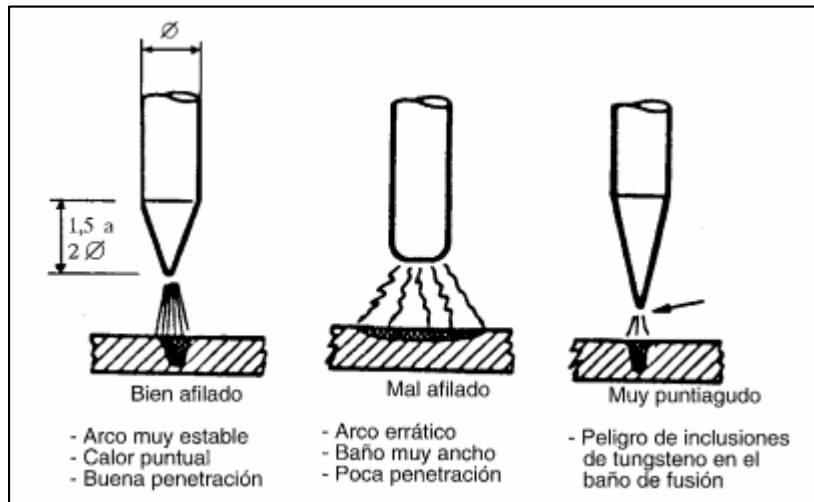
Acabados de la punta del electrodo en la soldadura GTAW
